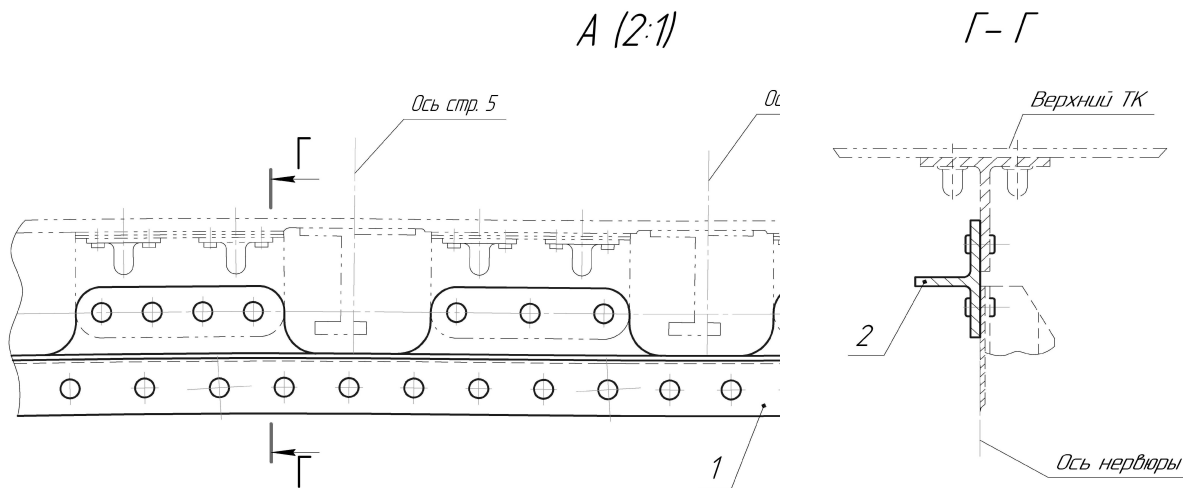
Фрагмент чертежа типовой конструкции пояса сборной нервюры:
